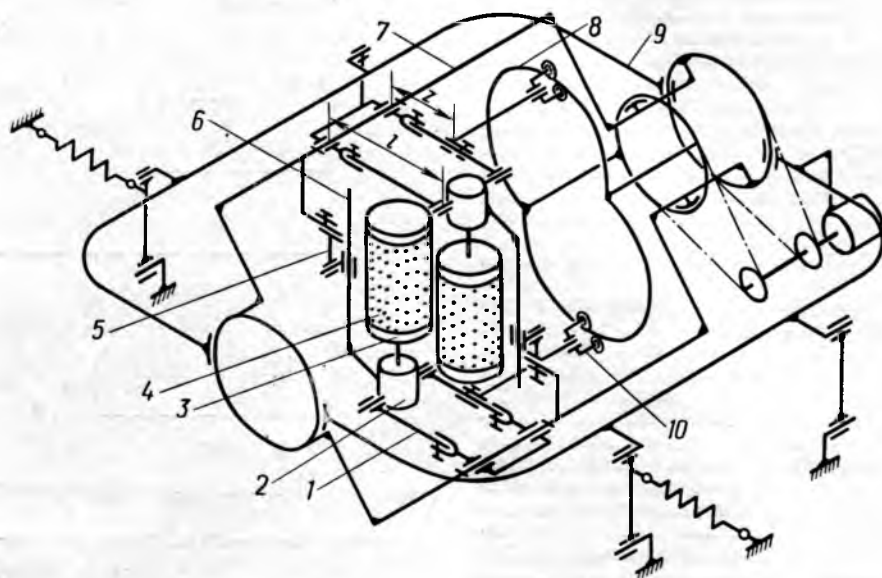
Кинематическая схема механизма продольных перемещений шлифовальных инструментов опытного образца линии, внедренного в производство
